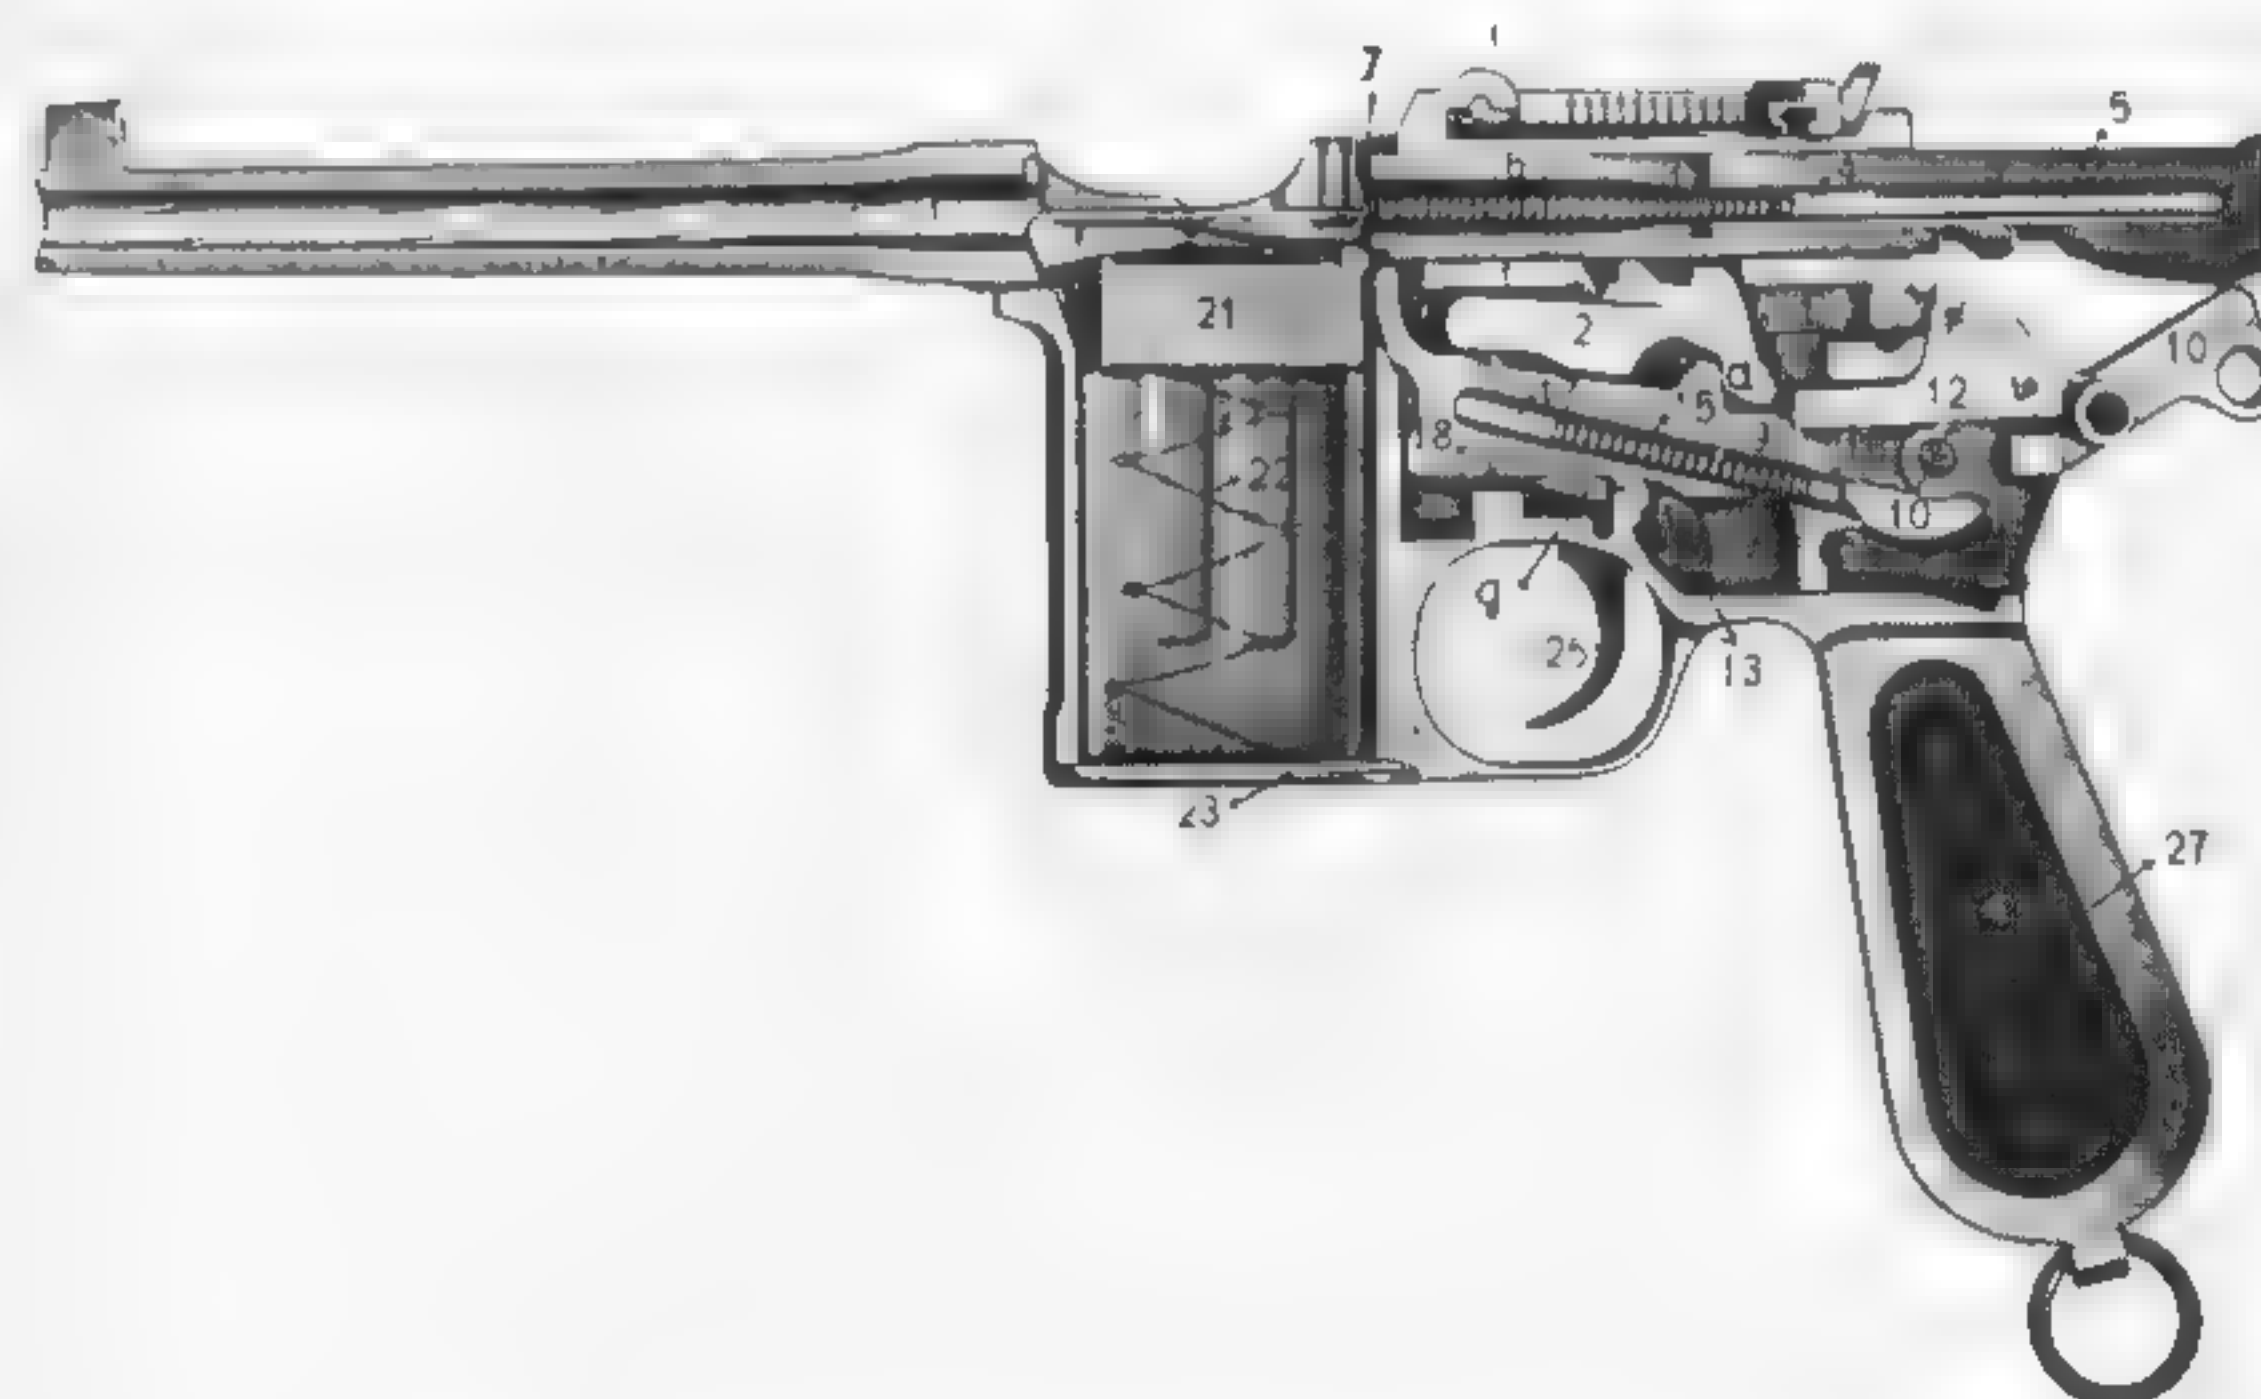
Längsschnitt der Pistole mit geöffnetem Verschuß
